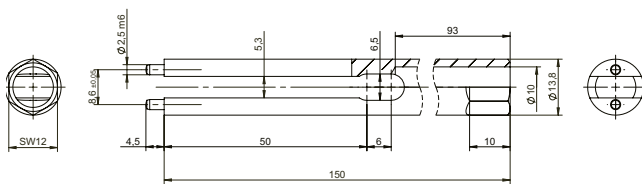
Montageschlüssel Ø13,8/SW12 Typ 1300A5 für Einbaubohrung > Ø14 mm
